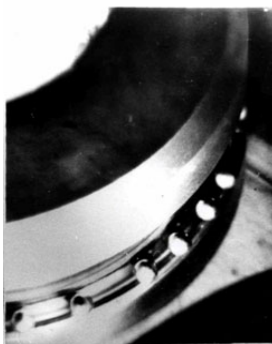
Фотография рабочей зоны станка для магнитно-абразивной обработки шариков.
